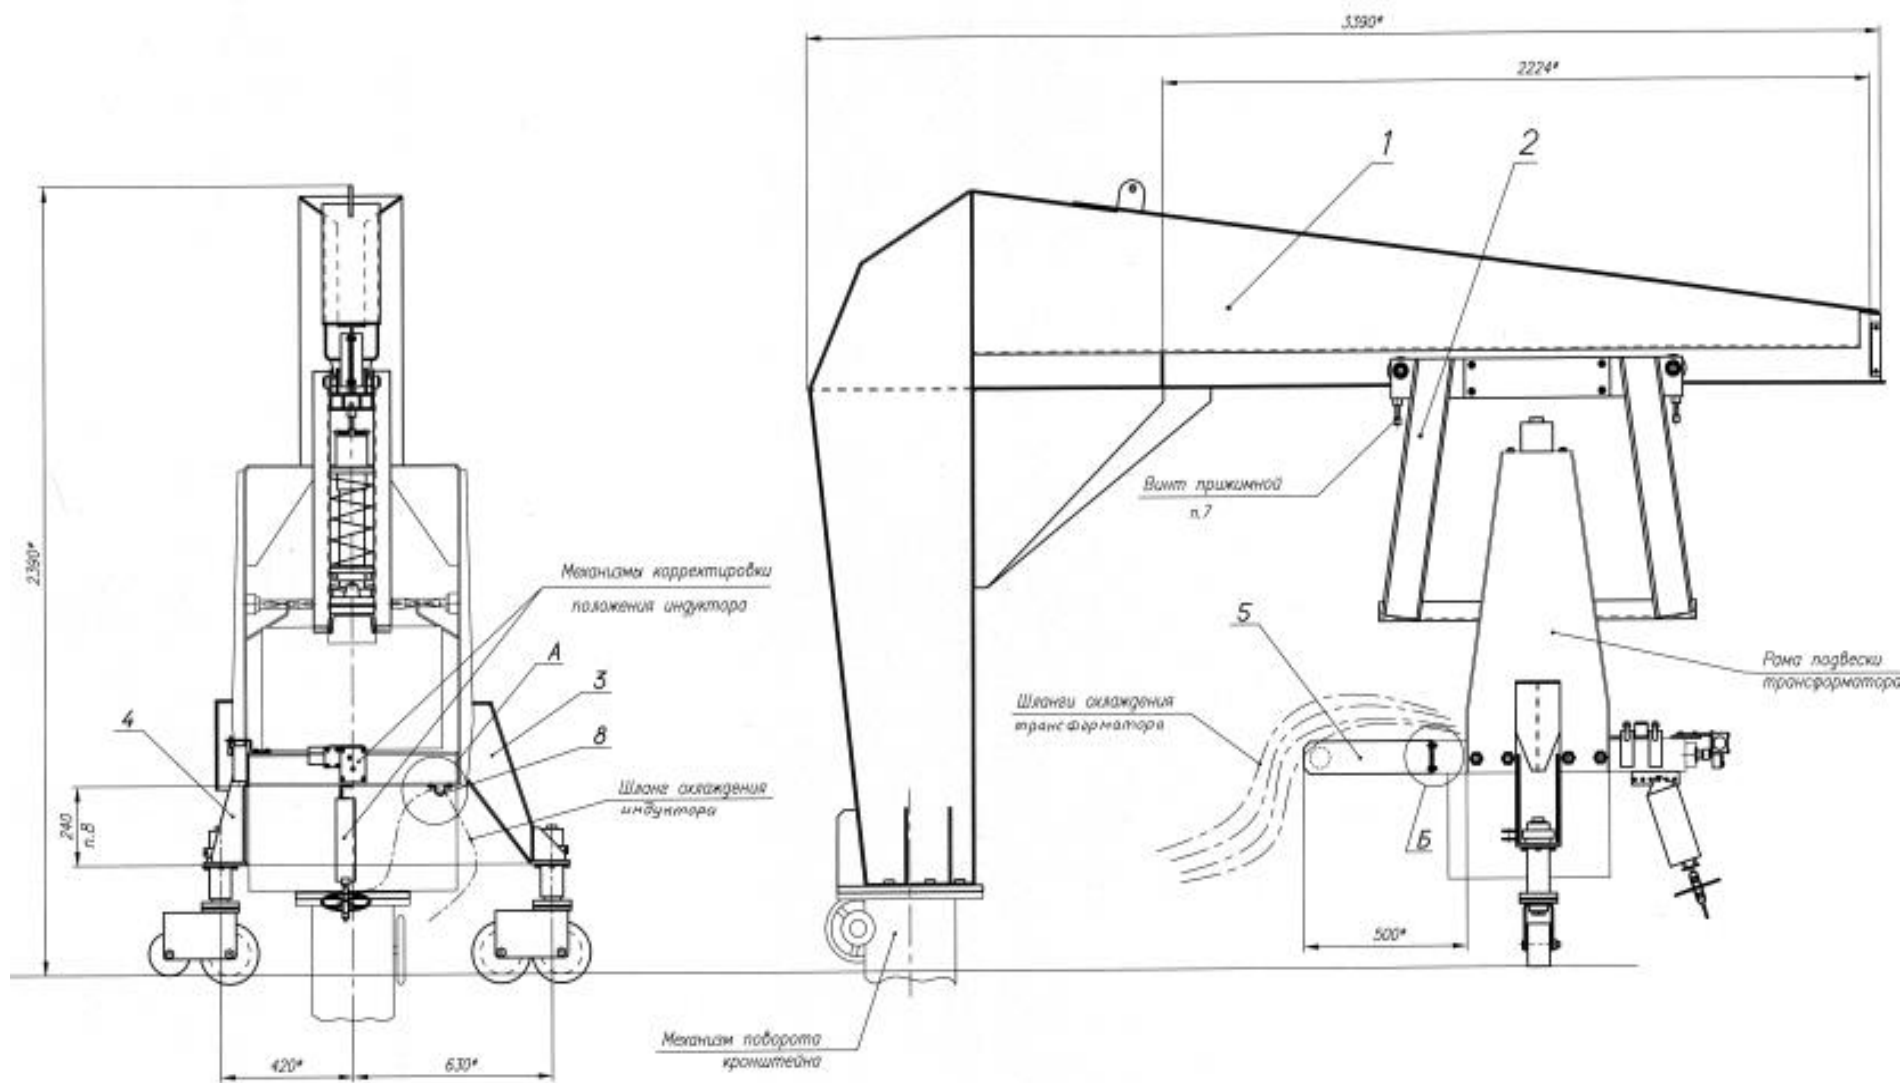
Оснастка для профилегибочного станка СКМЗ ТВЧ
